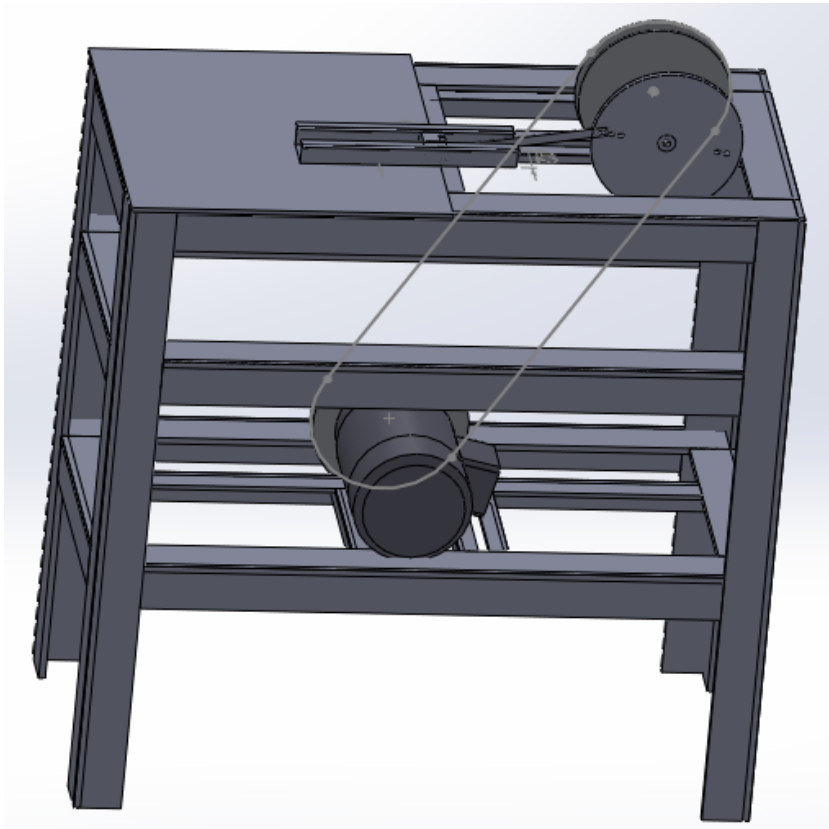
Vista de los conjuntos de las piezas construidas y ensambladas. Fuente: Autor.
